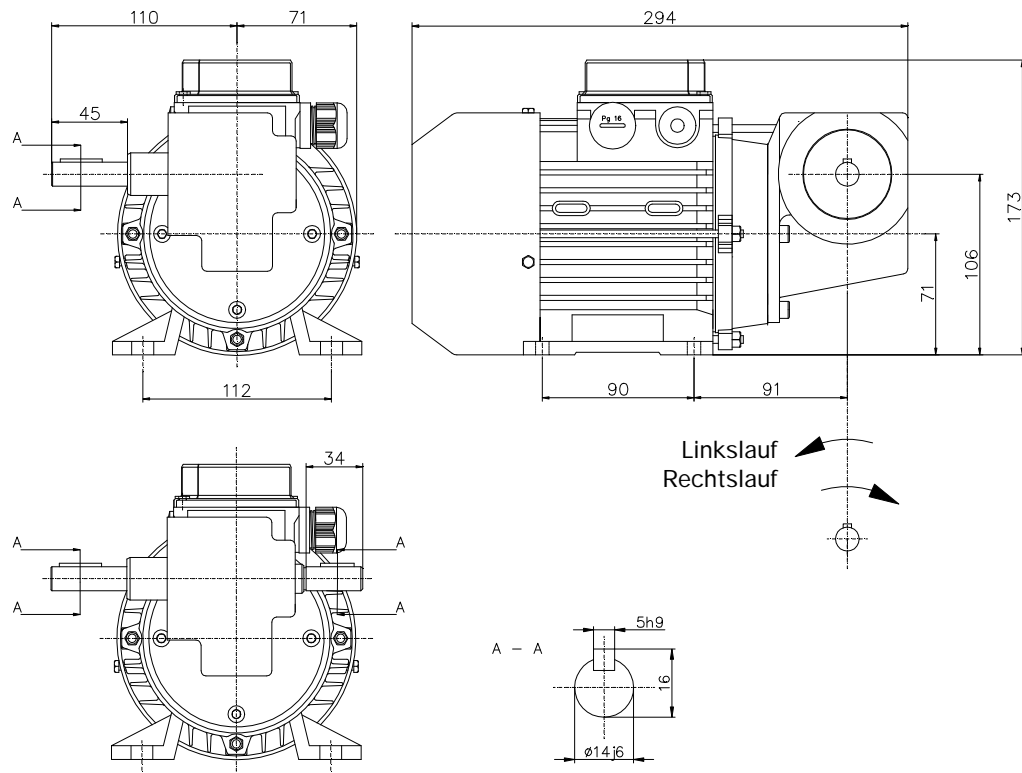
Motorabmessungen EMS-VVX 4 mit einer oder zwei Wellen
